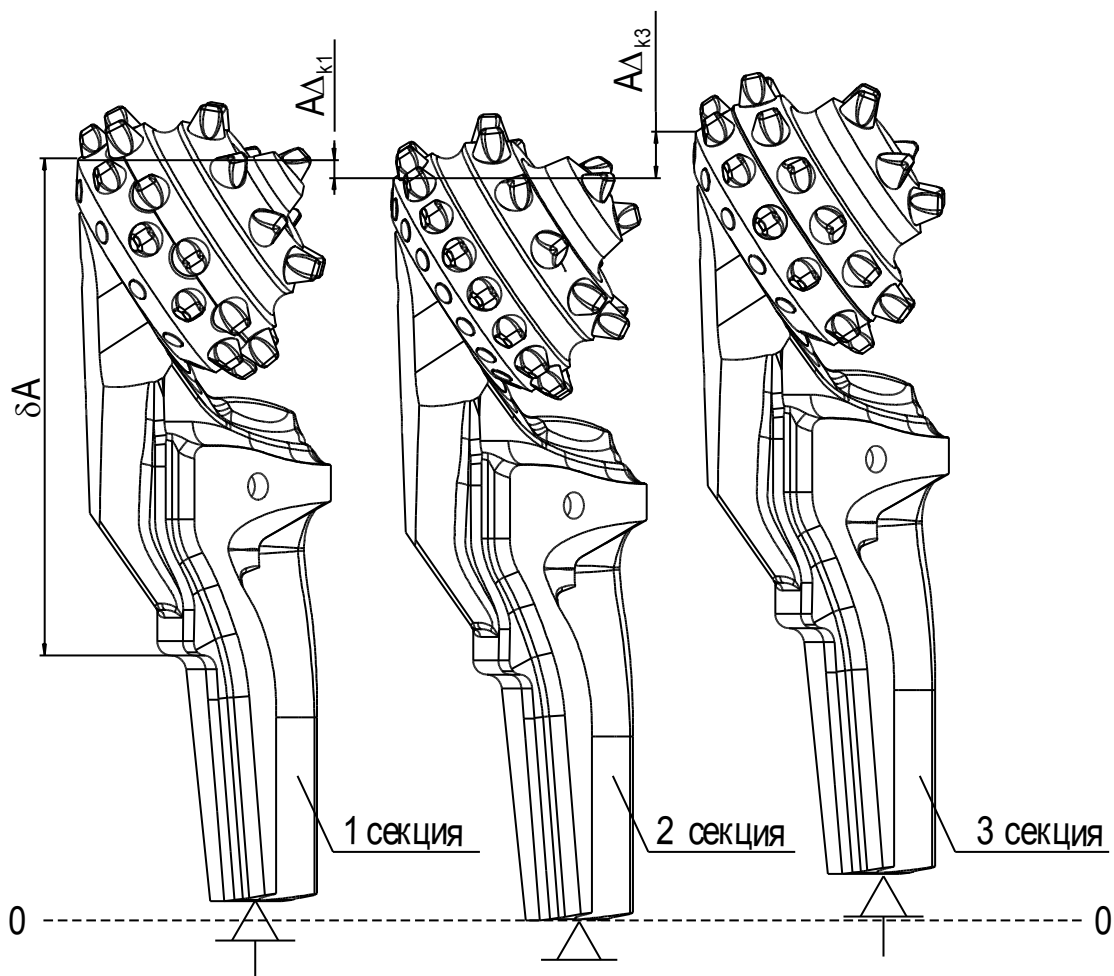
Развертка размерной цепи сборки трехсекций под сварку
